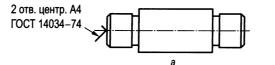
Обозначение центровых отверстий на рабочем чертеже:
